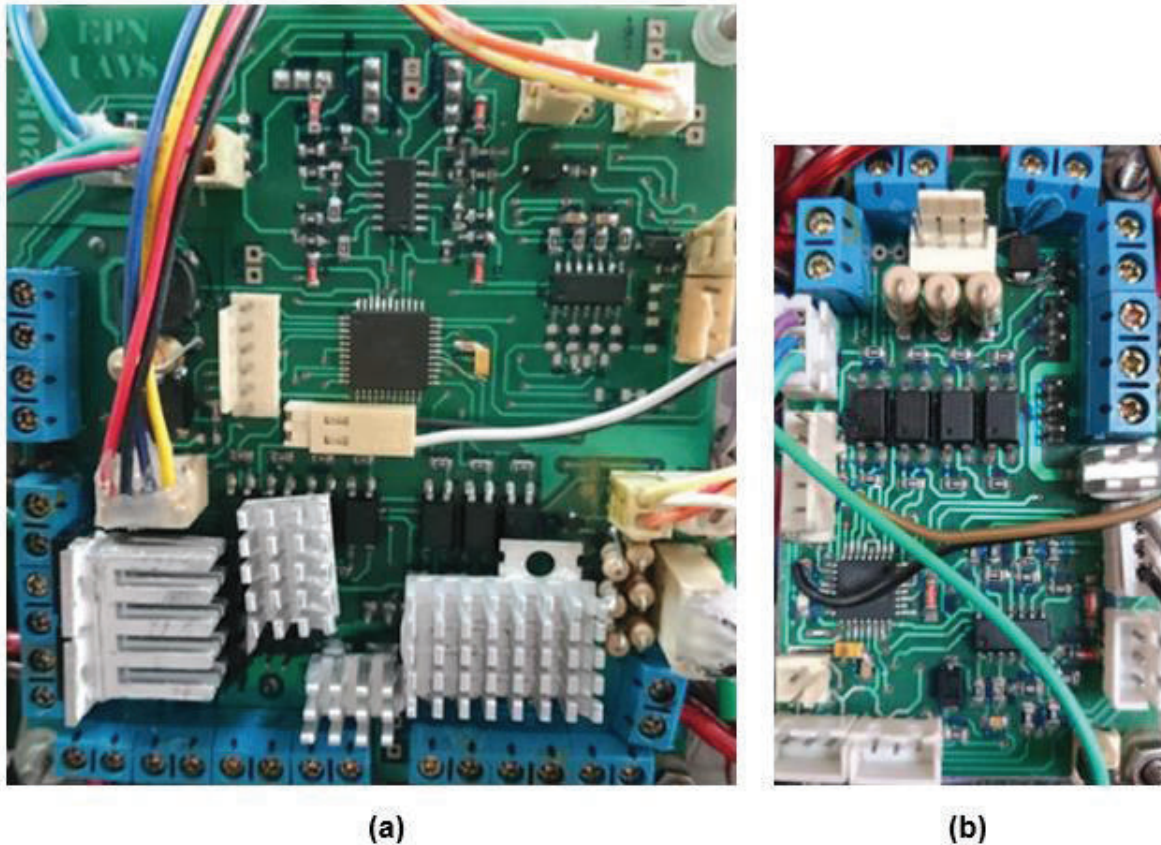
Placas de control desarrolladas: (a) parte 1 del equipo. (b) parte 2 del equipo
